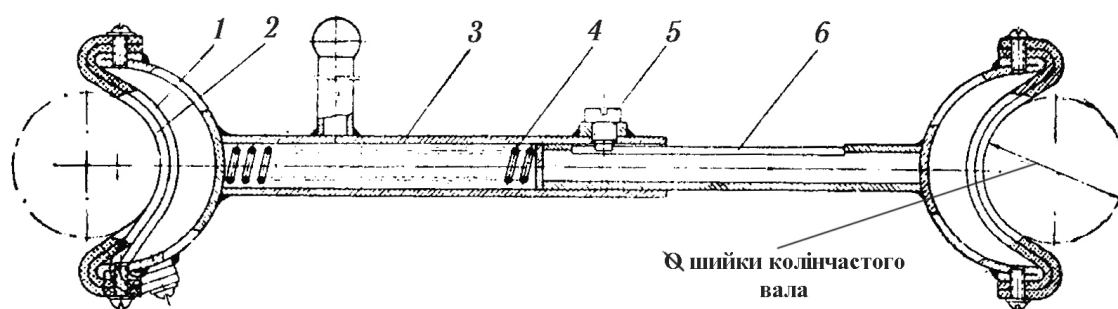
Хомут у зборі до верстата для полірування шийок колінчастих валів: 1 - стрічка шкіряна; 2 - стрічка фетрова; 3 - хомут; 4 - пружина; 5 - гвинт; 6- хомут.
